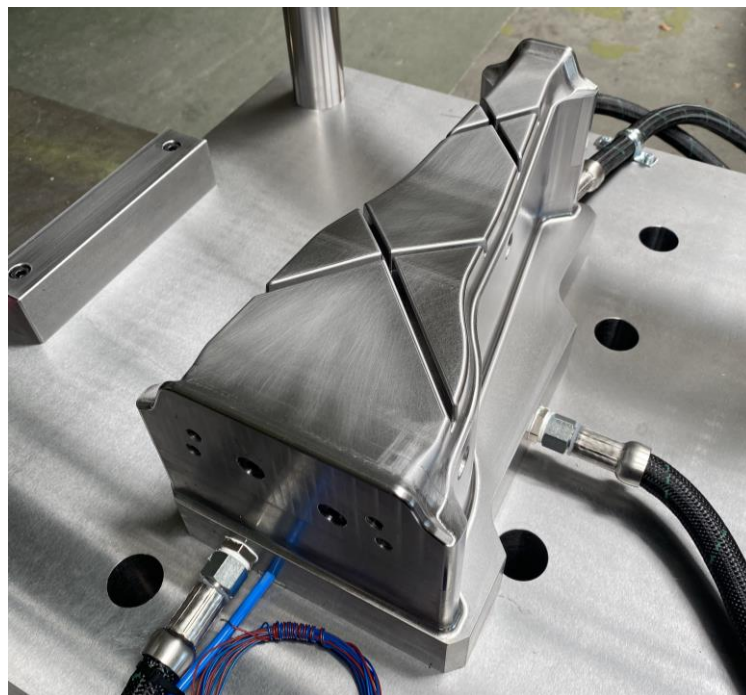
komplexe Geometrie Werkzeugstempel [Quelle: Schmidt Modellbau GmbH]
